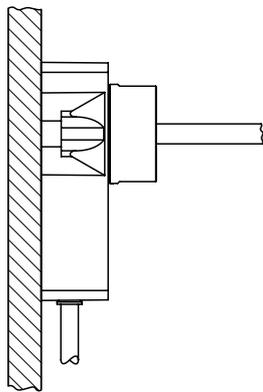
Positionsgeber auf dem Sensorgehäuse montieren
